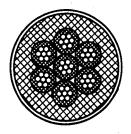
Поперечный разрез семижильного кабеля марки КМВВЭ
